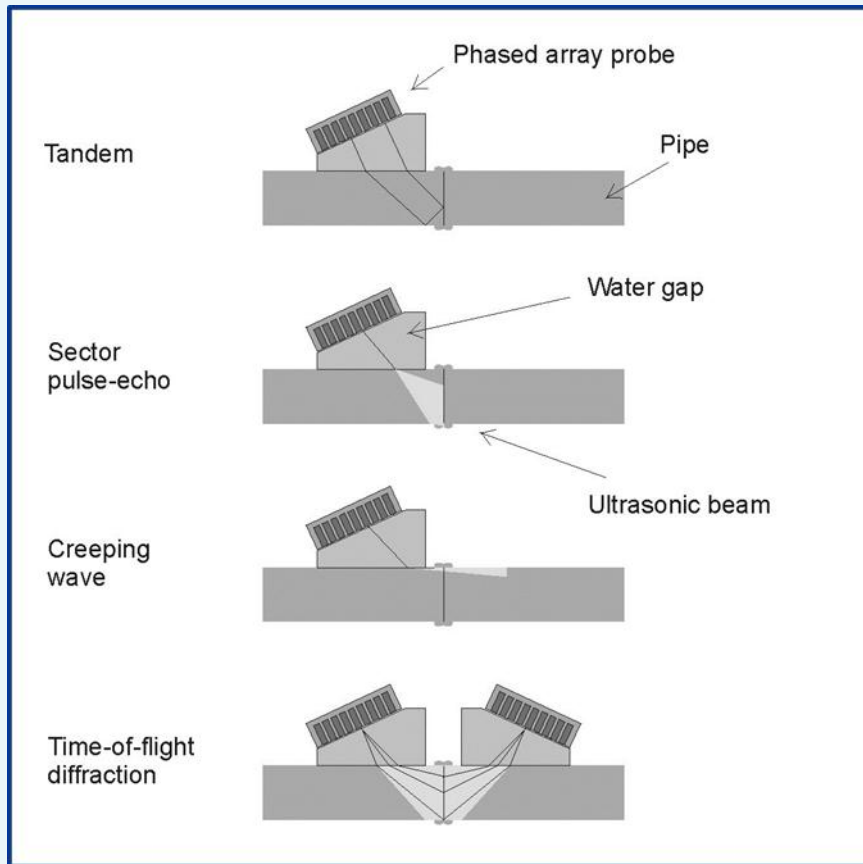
Esquema de diferentes técnicas de inspección de soldaduras a tope
